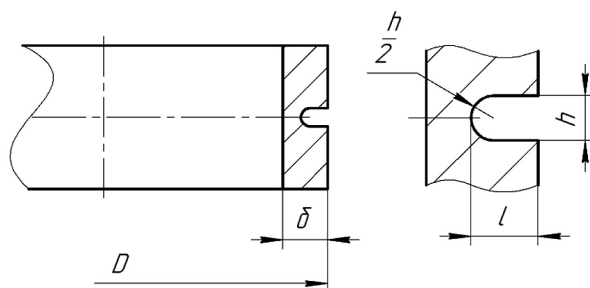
Модель заготовки с поперечной канавкой на наружной поверхности
